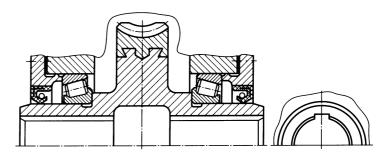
Выходной полый вал навесного червячного редуктора
